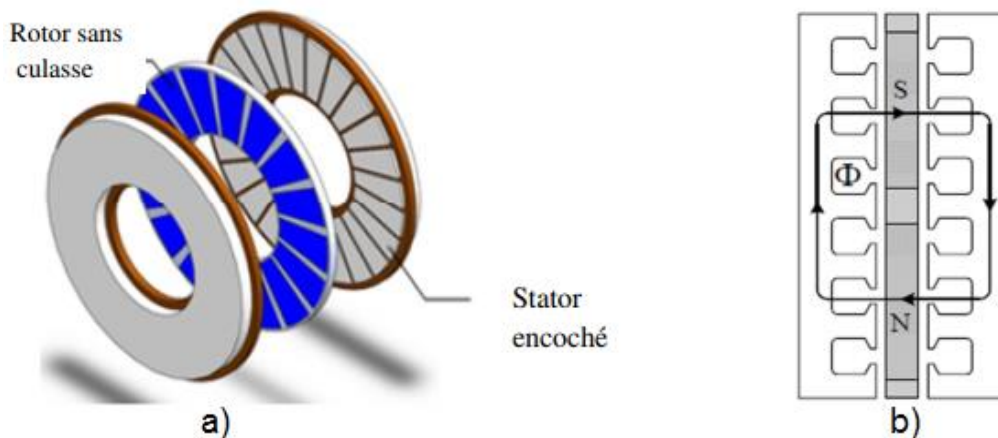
Machine à flux axial double stator-rotor a) avec bobinage encoché b) circulation de flux [23], [22]
